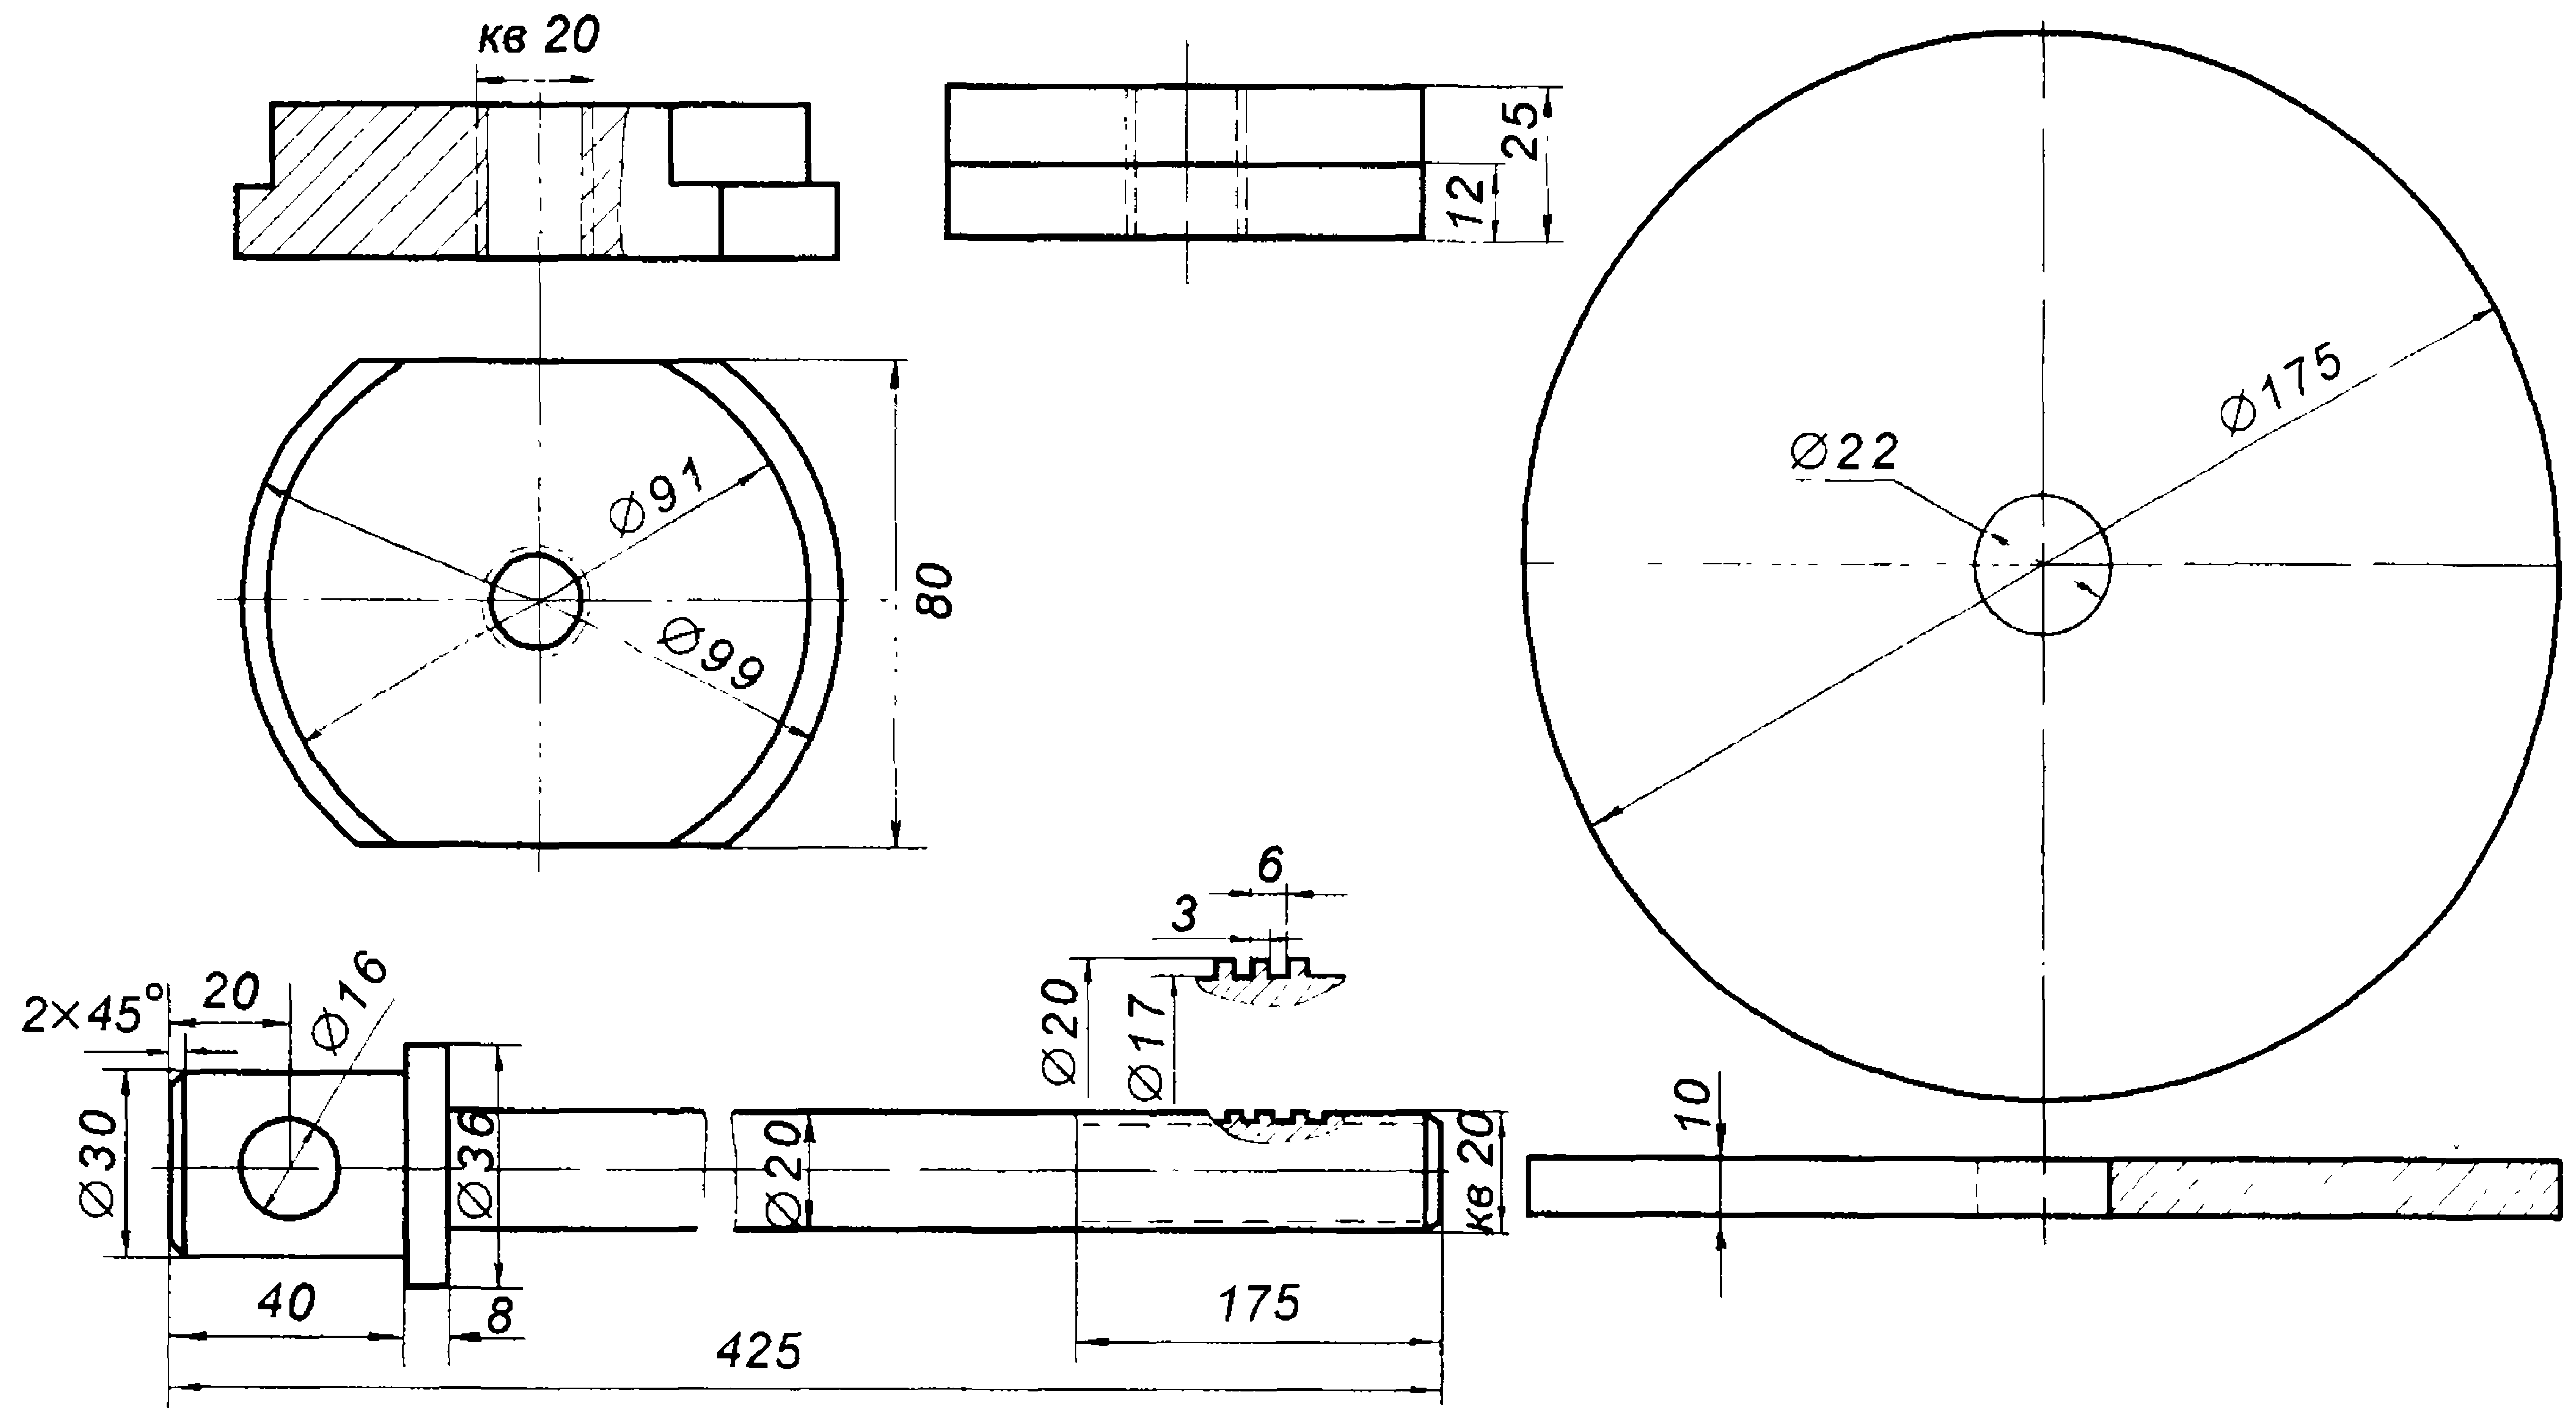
Съемник для выпрессовки гильз из блока цилиндров
